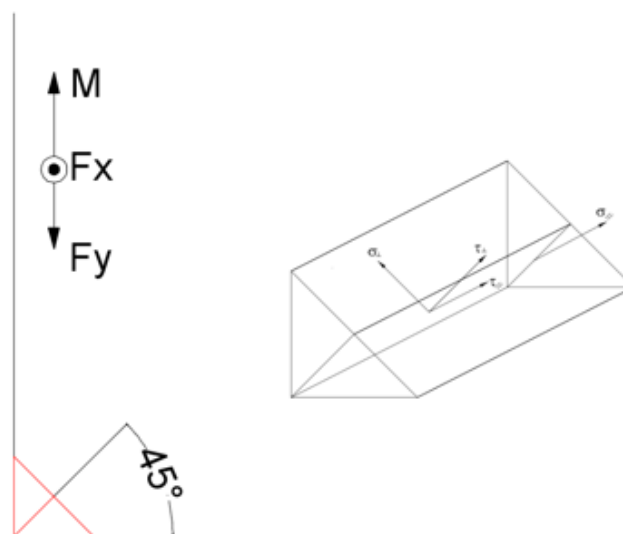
Descomposición de fuerzas al plano de la soldadura
